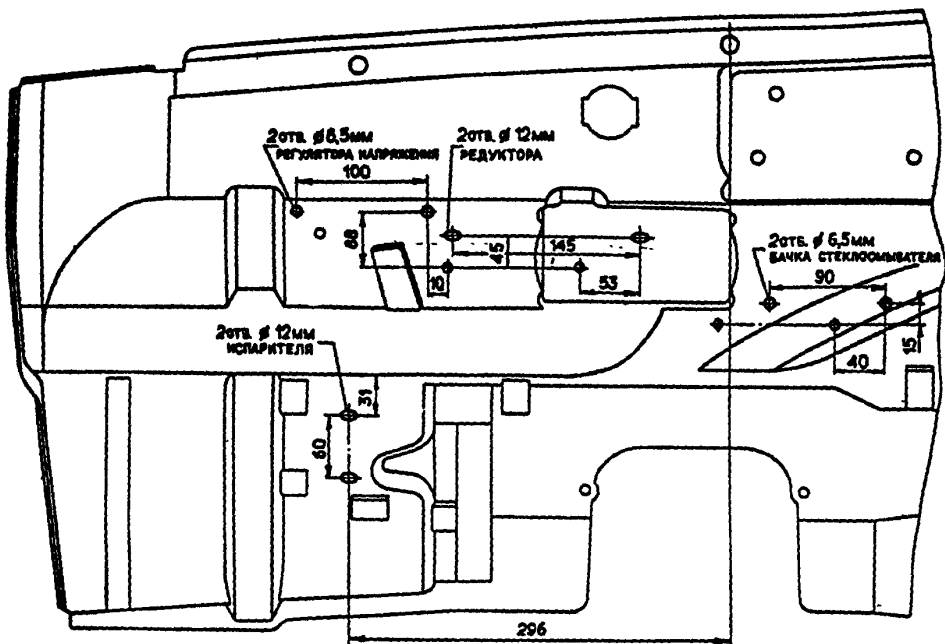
Разметка отверстий на брызговики правого переднего крыла для крепления газового редуктора, испарителя, кронштейна бачка стеклоомывателя и регулятора напряжения
